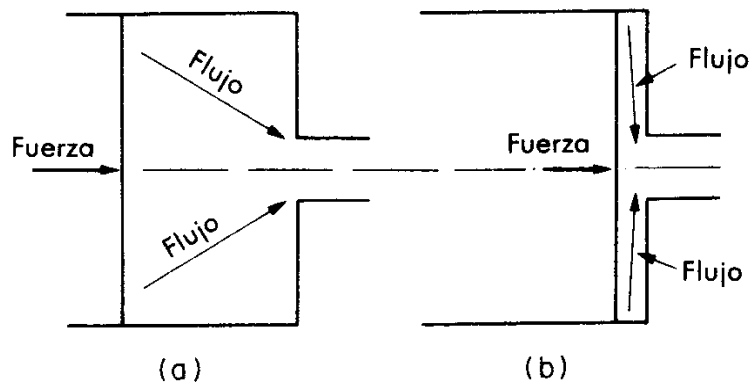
Esquema del flujo y la fuerza en un proceso de extrusión.
